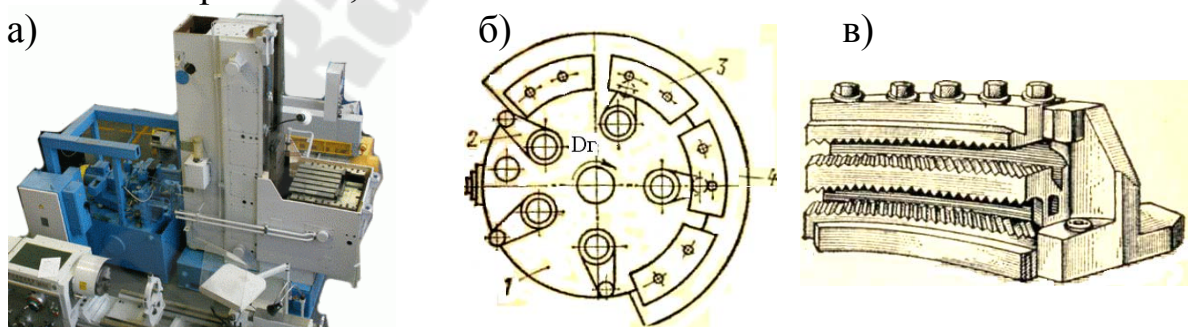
Общий вид вертикально-протяжных станков (а), схема протягивания плоскости на станке непрерывного действия (б) и вид держателя с протяжками (в)
